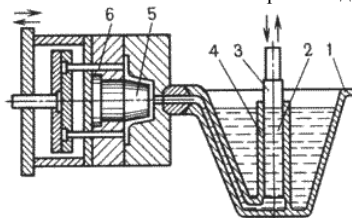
Схема изготовления отливки на машинах с горячей камерой прессования
